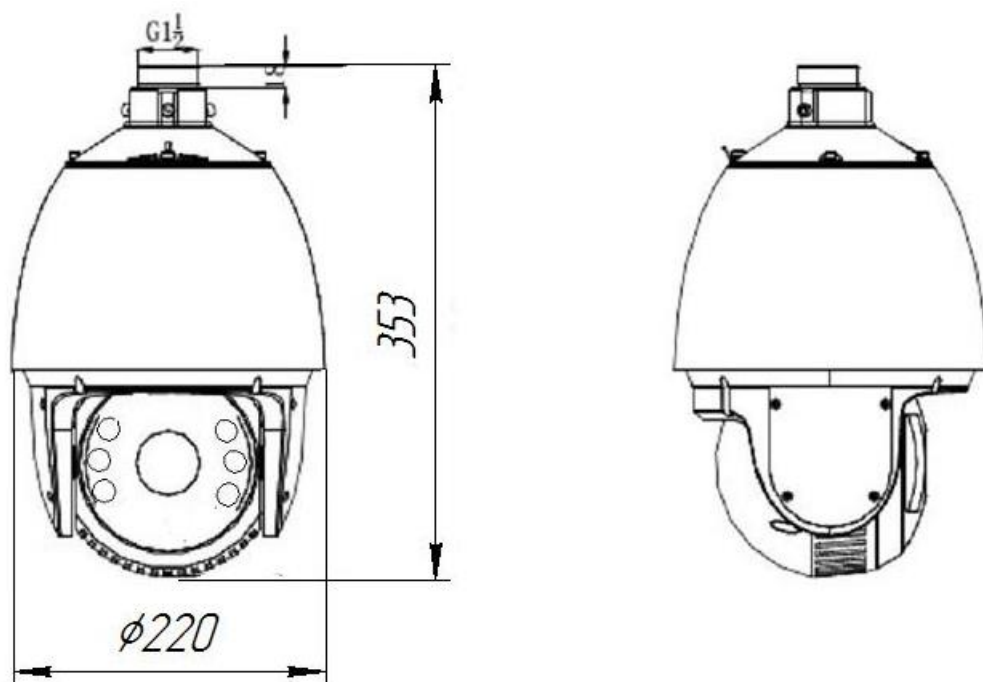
Габаритные размеры поворотной видеокамеры СВК-850
